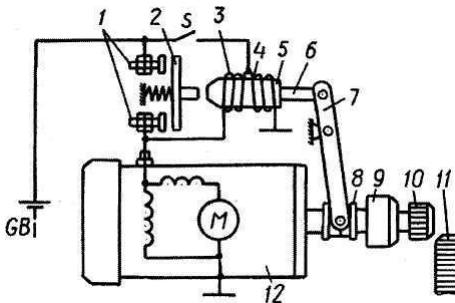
Схема керування електростартером: 1 – силові контакти; 2 – рухомий контактний диск; 3, 4 – обмотки тягового реле; 5 – якір тягового реле; 6 – шток; 7 – важіль приводу; 8 – повідкова муфта; 9 – муфта вільного ходу; 10 – шестірна приводу; 11 – зубчастий вінець маховика; 12 – електродвигун
